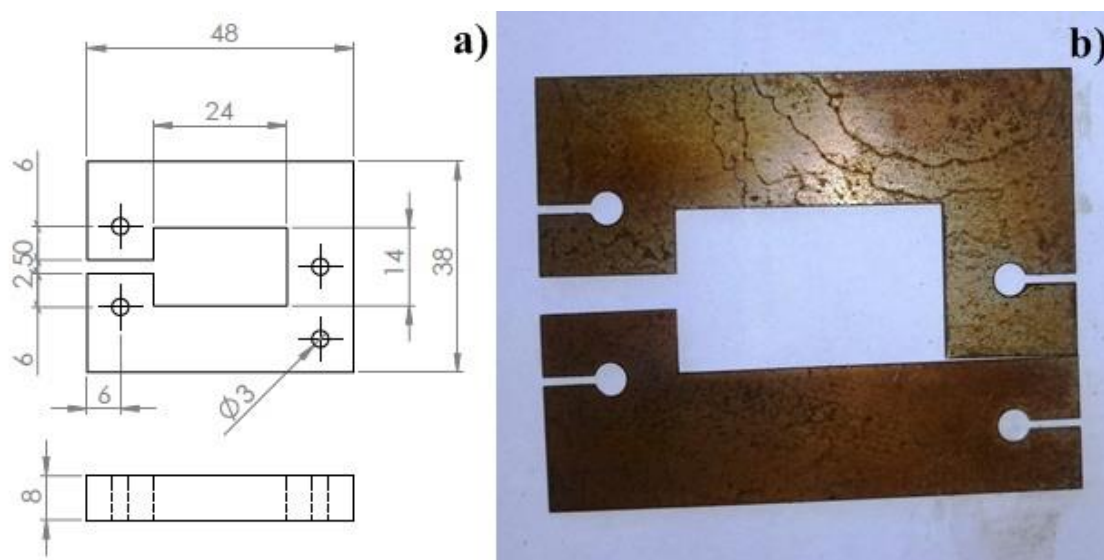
Circuito magnético: a) desenho das dimensões b) chapa cortada.
